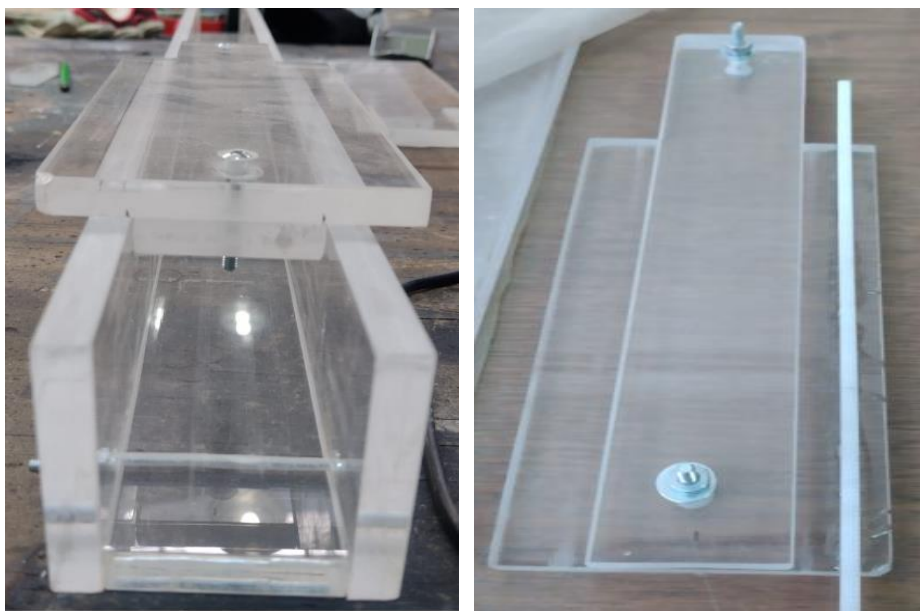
a) Montaje del sistema sobre la zona de desplazamiento. b) Pegado del riel de engranajes a la base del sistema.
